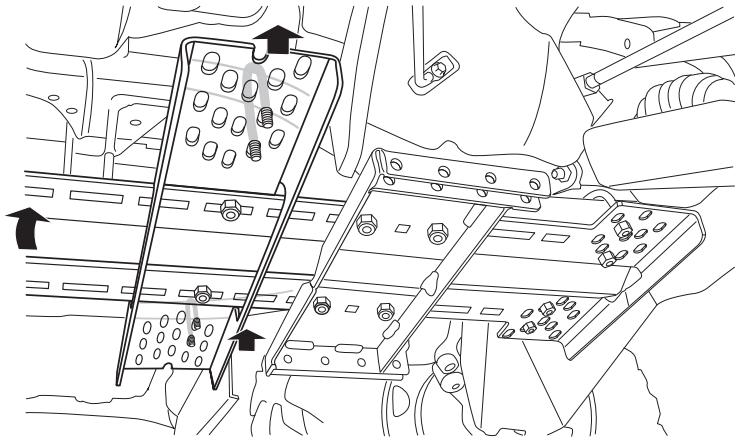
Fissare senza serrare la piastra di contatto posteriore ai bulloni a testa tonda posteriori con i dadi di fissaggio.
